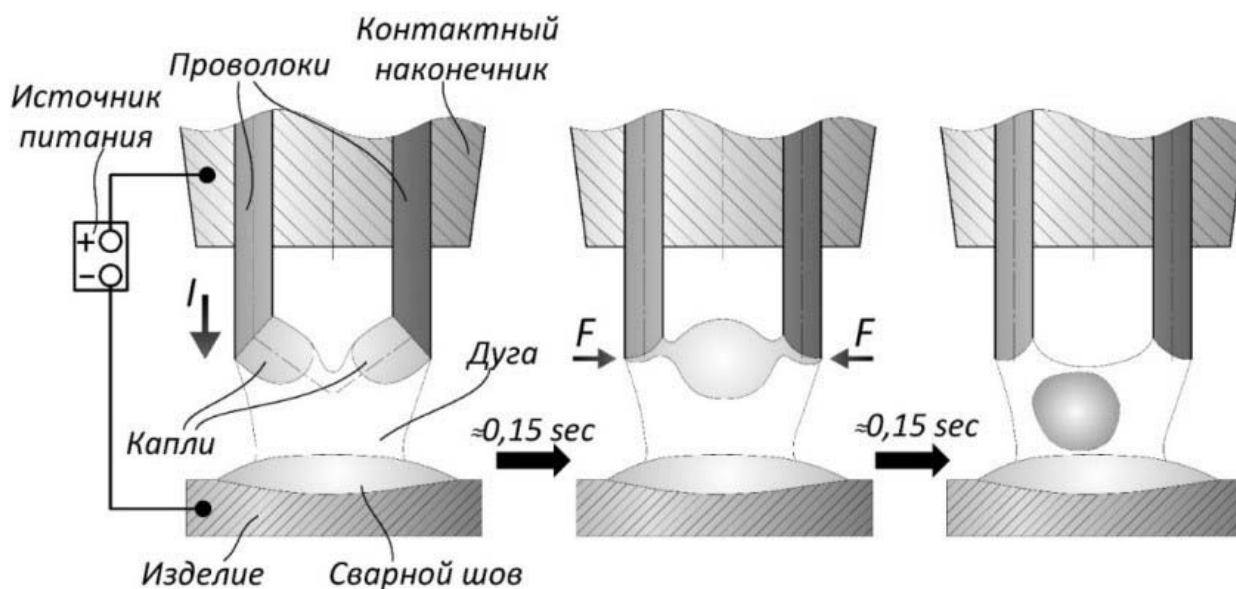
Кинетика процесса образования общей капли и сварочной дуги первого типа ($I = 330 \text{ A}$; $U = 26 \text{ В}$)
